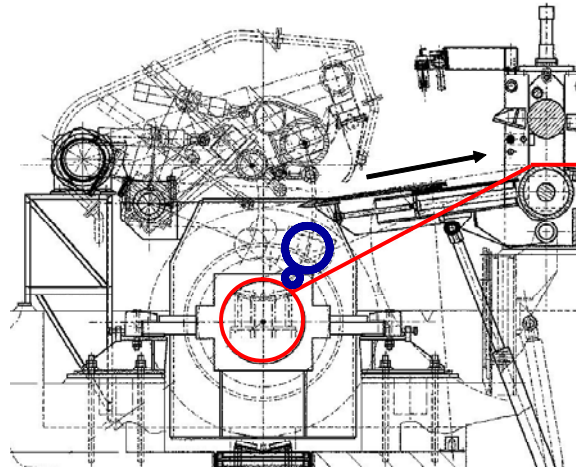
Desbobinadeira do laminador de acabamento com o rolo de pressão apoiado sobre a tira.
